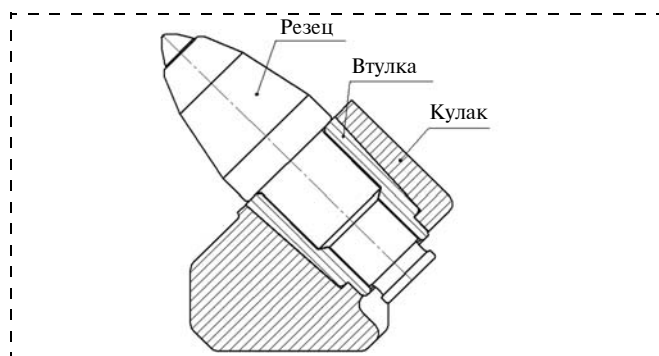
Тангенциальный поворотный резец и кулак с втулкой
